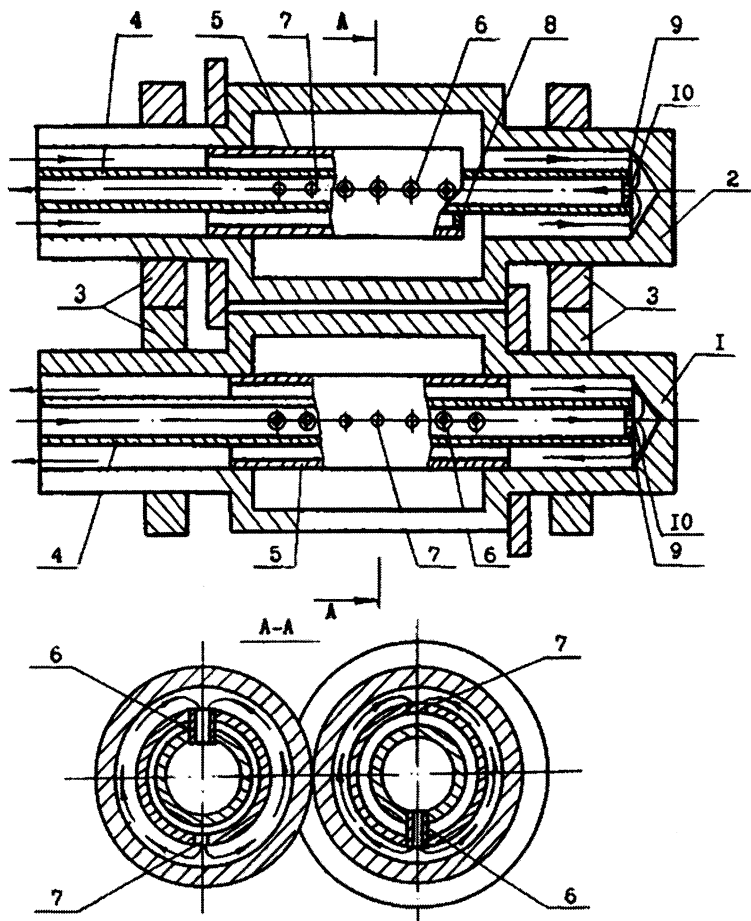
Принципиальная схема конструкции валкового кристаллизатора
